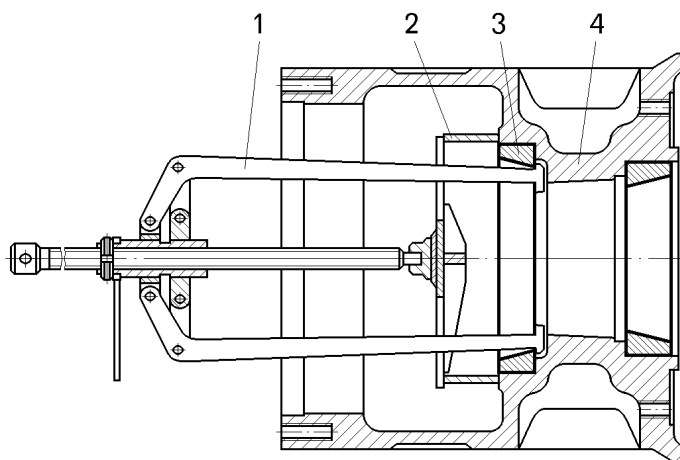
Выпрессовка наружных колец подшипников из ступицы колеса:
